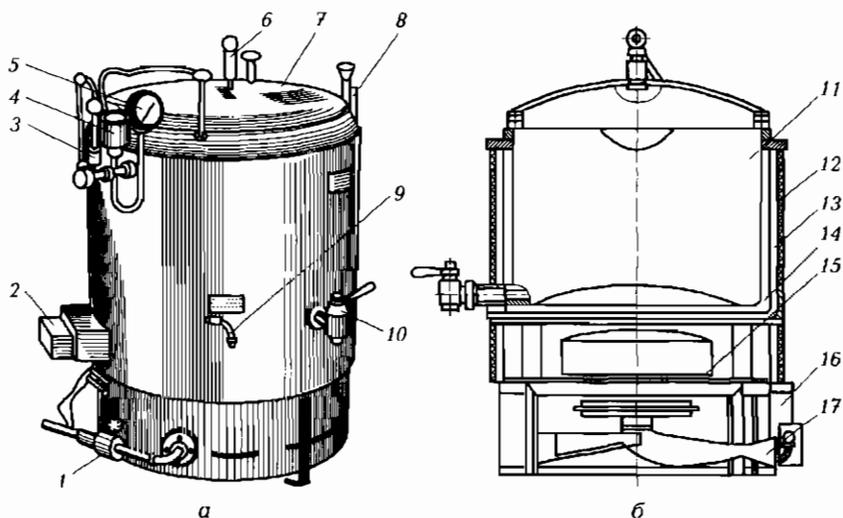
Котел пищеварочный газовый КПГ-160:
